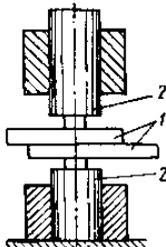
Схема сварки без предварительного зажатия свариваемых деталей.
